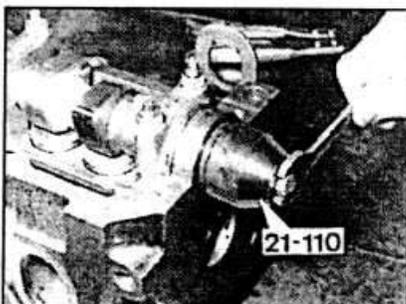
Е.24. Установка уплотнительного кольца распределительного вала при помощи специального приспособления.
